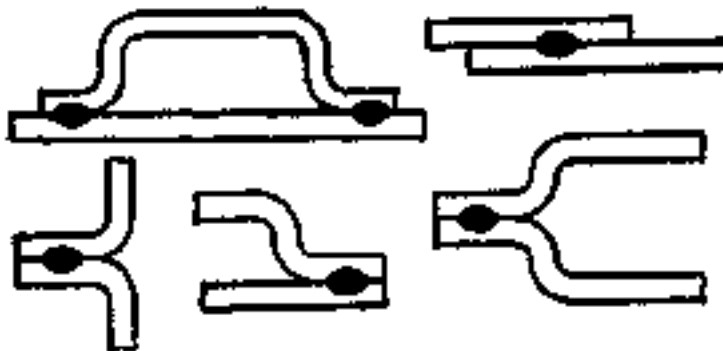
Типы сварных соединений точечной сварки
